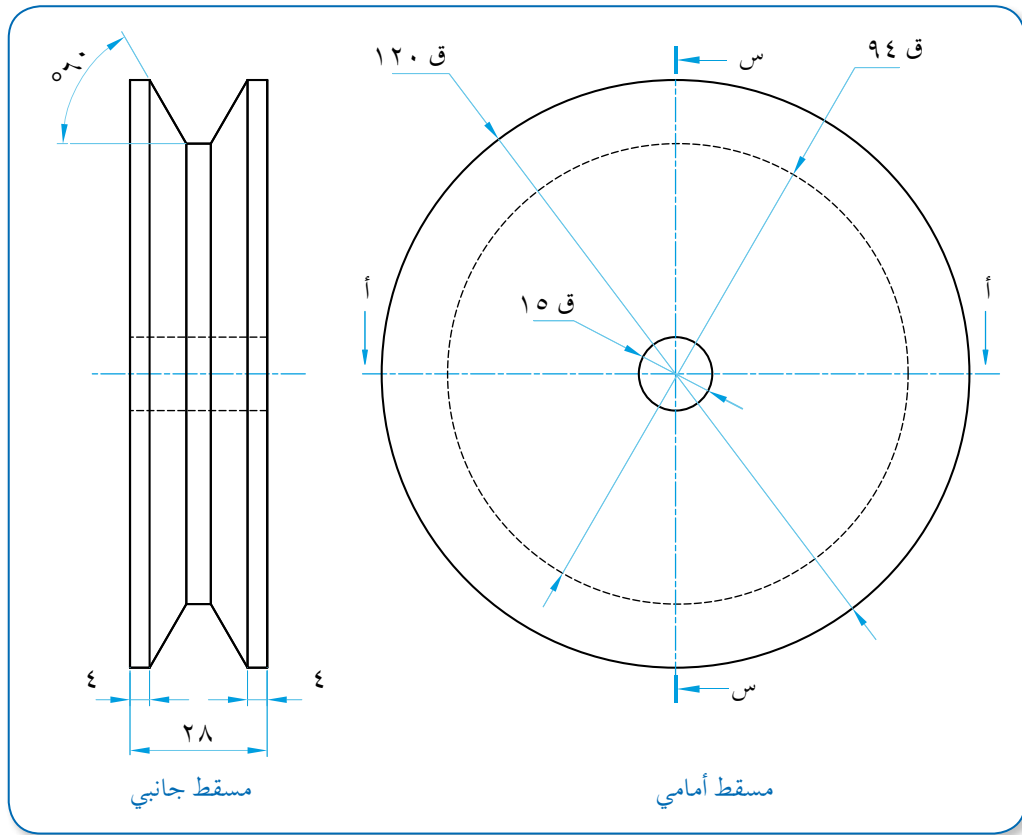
مسقط أمامي ومسقط أفقي لجسم ساحة.
